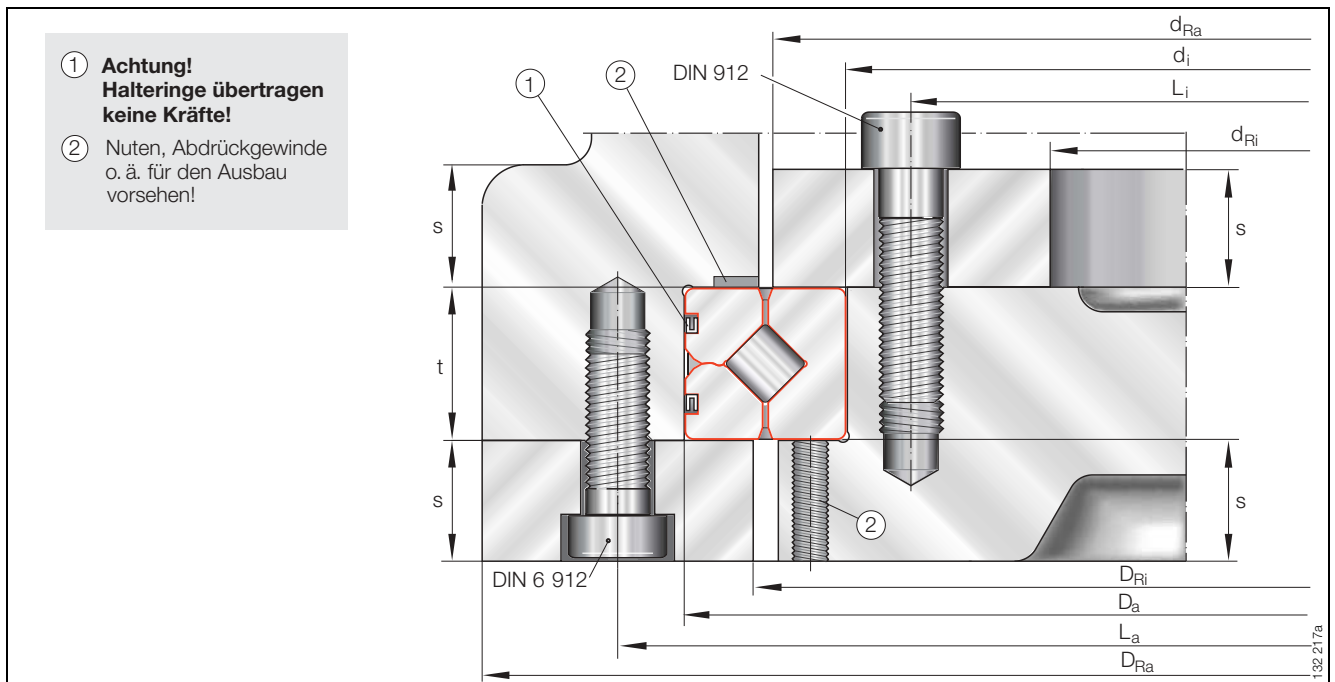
· Gestaltung der Lagerung – Anschlussmaße
